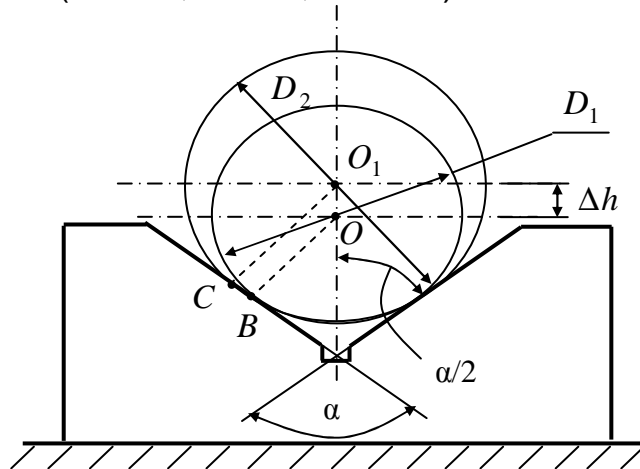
Схема визначення похибки базування циліндричної заготовки в призмі
